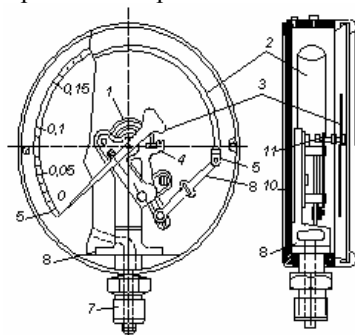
Манометр: 1 - пружини; 2 - стрілка; 3 - зубчастий привід; 4 - шарнір; 5 - плече; 7 - ніпель; 8 - стійка; 9 - шкала; 10 - корпус; 11 - зубчасте колесо.
